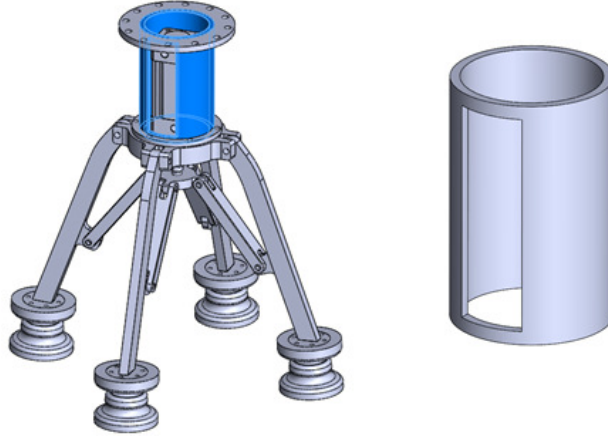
Lastik Jant Tutucusu - Kovan Üst Flanş Tasarımı
